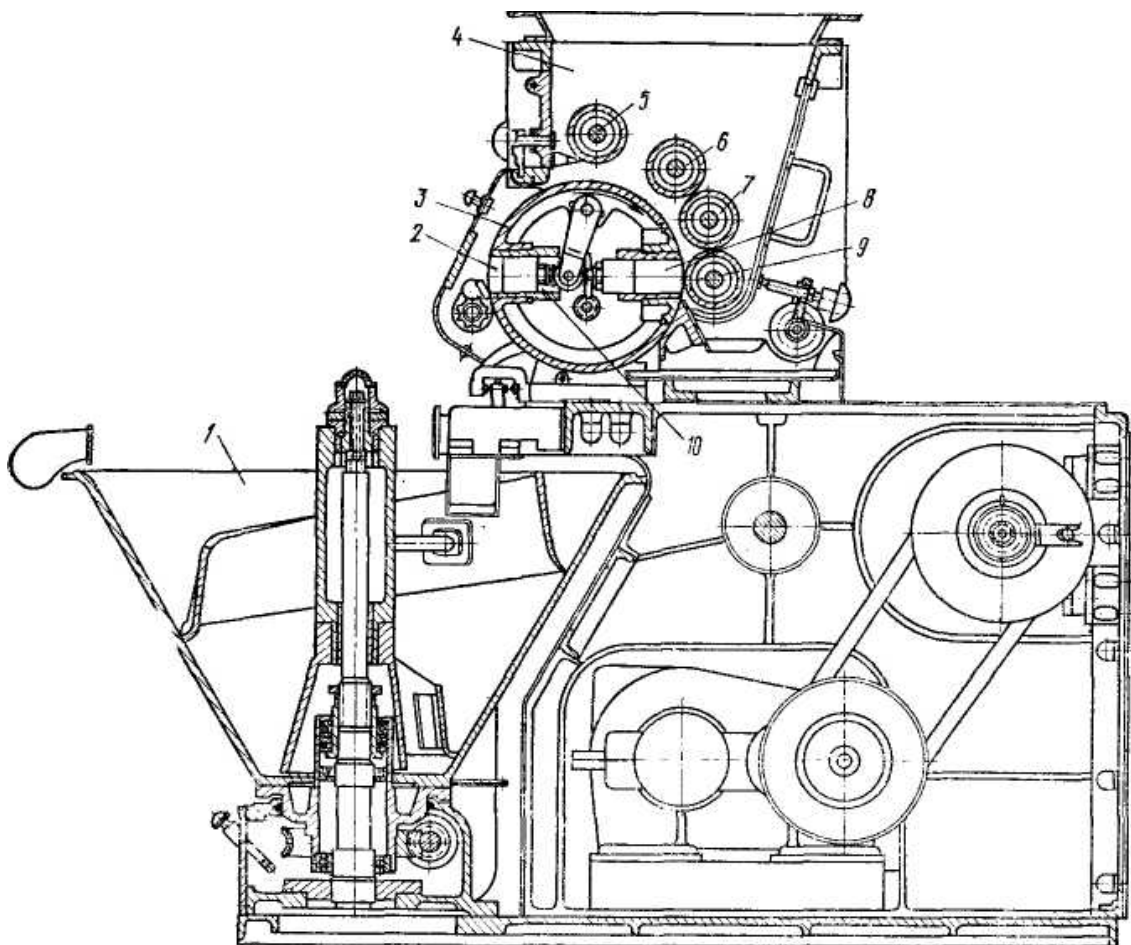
Ділильно-округлювальний агрегат ХЛС-9.
